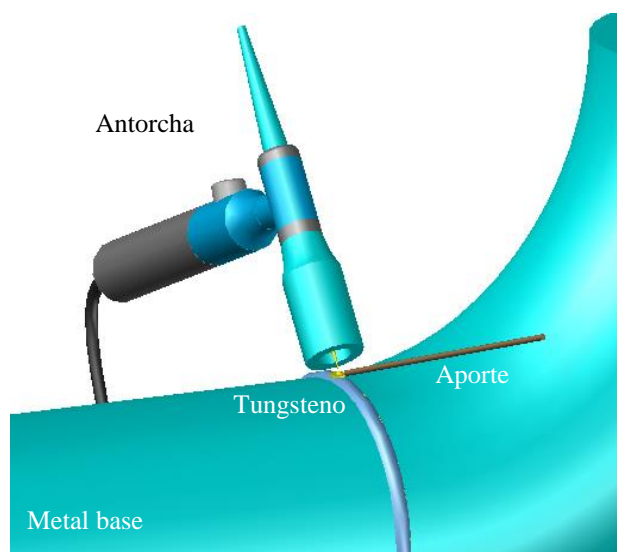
Esquema del proceso soldadura GTAW.
